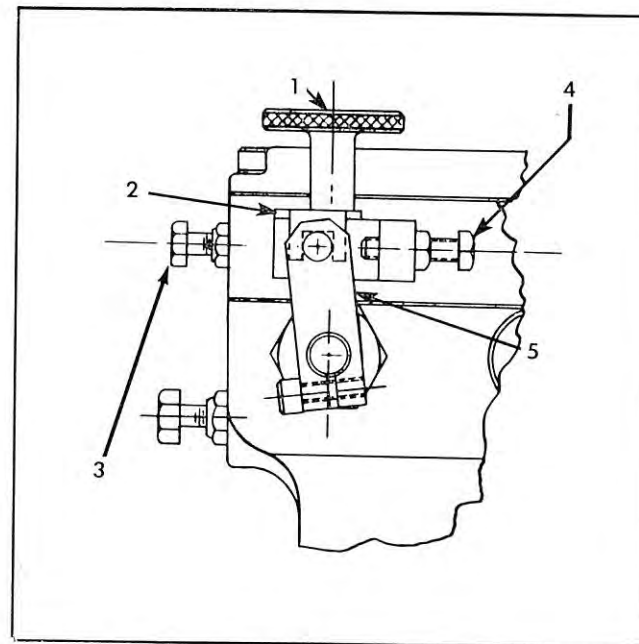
Réglage extérieur de la chute de vitesse régulateur P.S.G.
